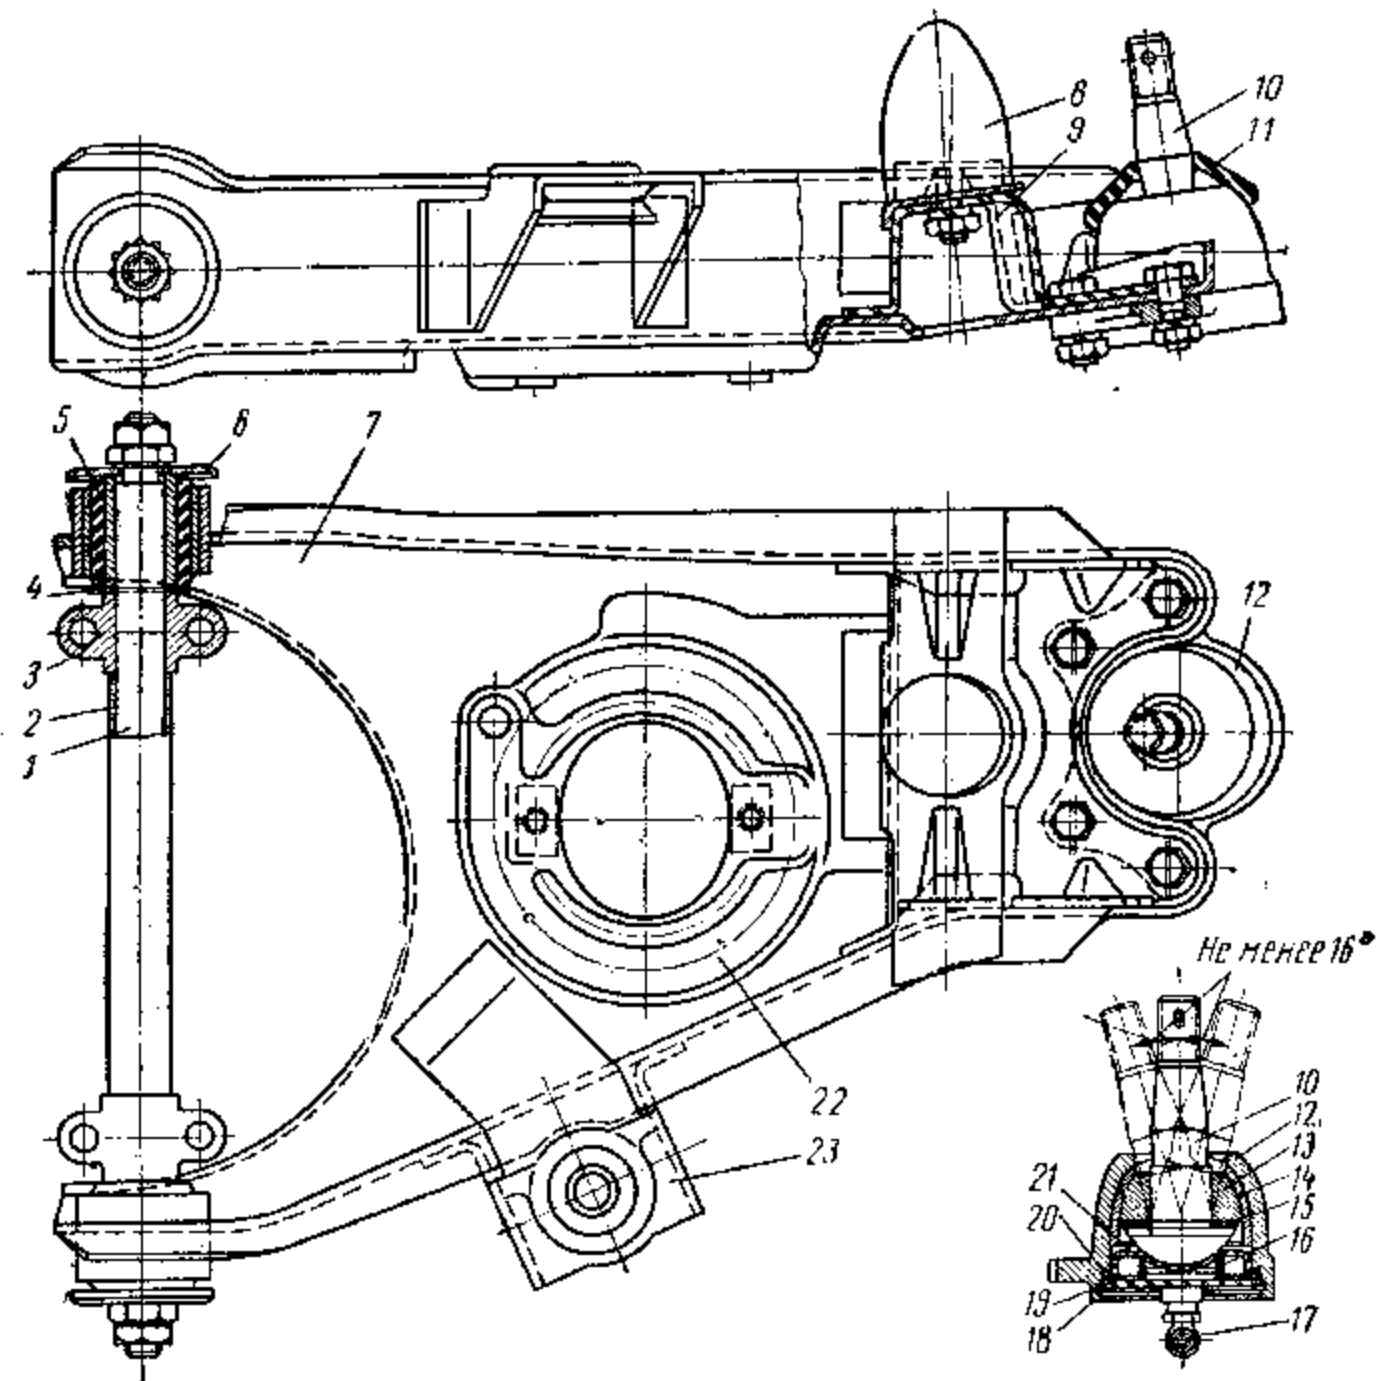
Верхний рычаг передней подвески в сборе с шаровым шарниром и осью:
